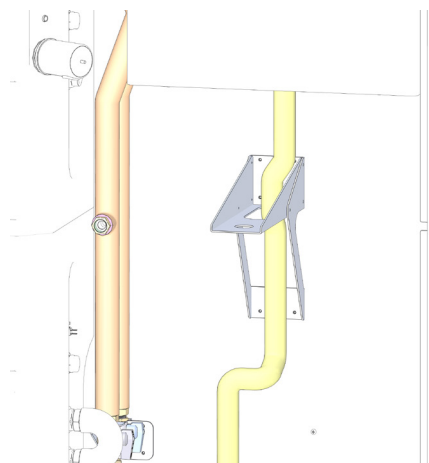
Dettaglio passaggio tubo gas alimentazione caldaia con kit solare
